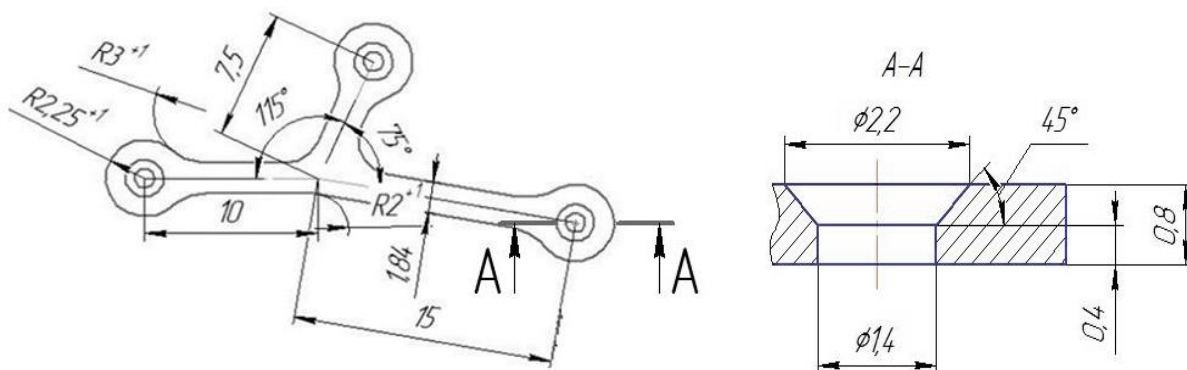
Конструкція та розміри У - пластини
